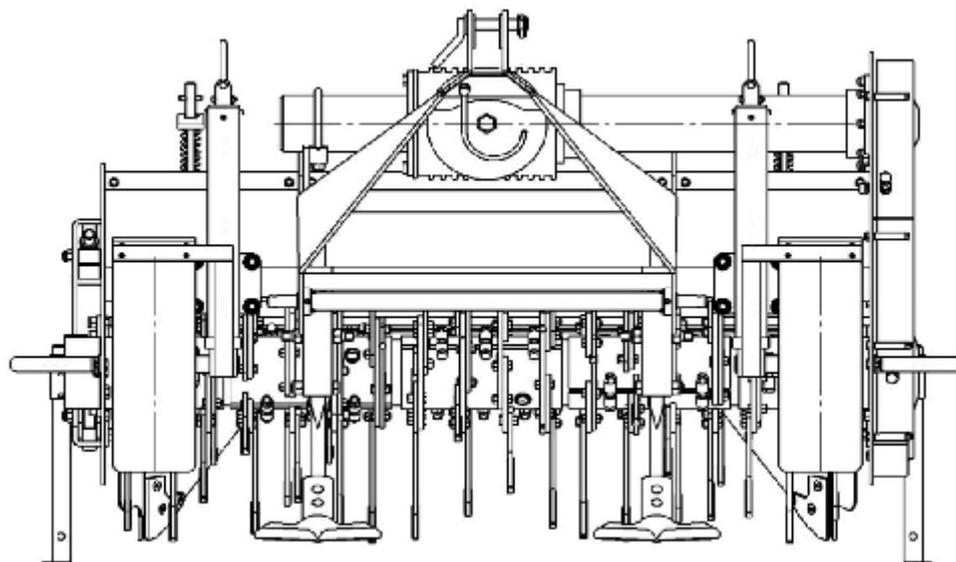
Культиватор-гребнеобразователь (вид спереди)
